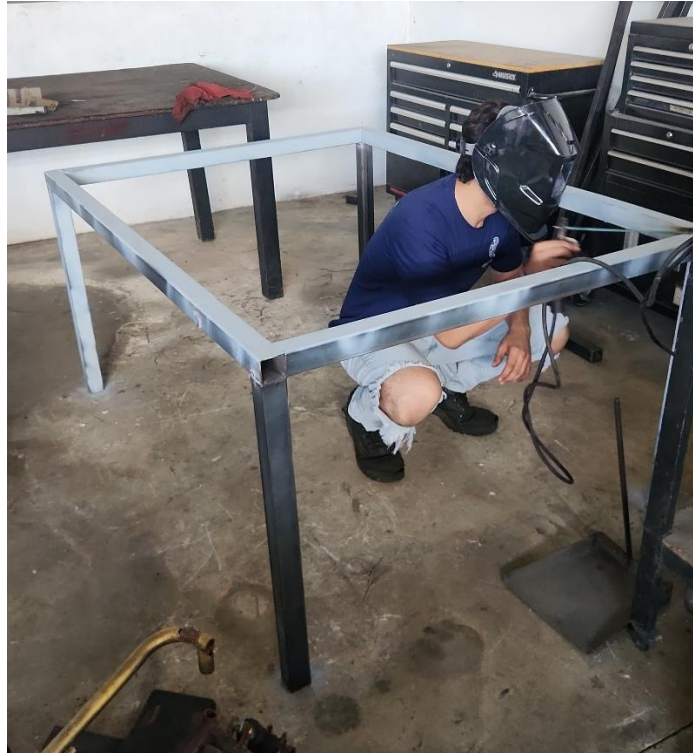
Soldadura de la base del banco de banco de pruebas
